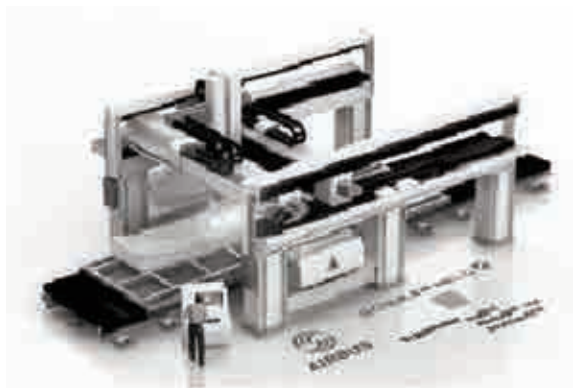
Опытная установка для лазерной сварки трехмерных деталей
